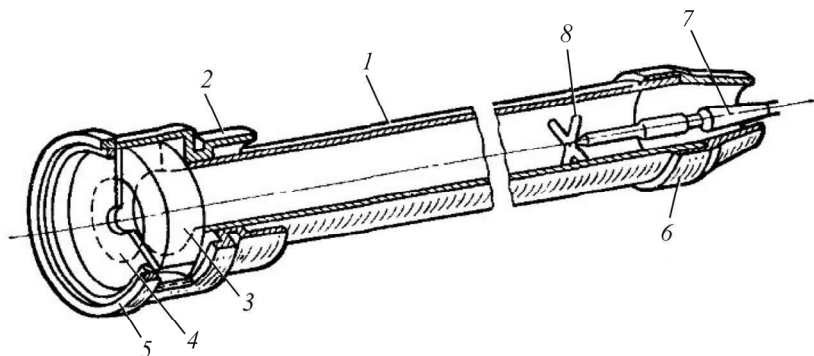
Вихревая трубка с торможением потока: 1 – камера разделения; 2 – корпус; 3 – улитка; 4 – диафрагма; 5 – гайка; 6 – сопло; 7 – регулировочная игла; 8 – крестовина
